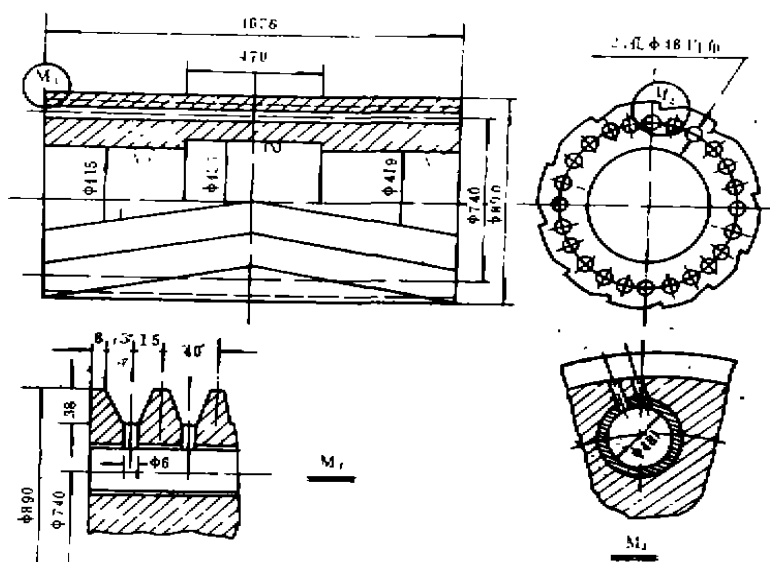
压榨甘蔗机的压榨辊 Fig 1 Sugar machine lotus mill roll
